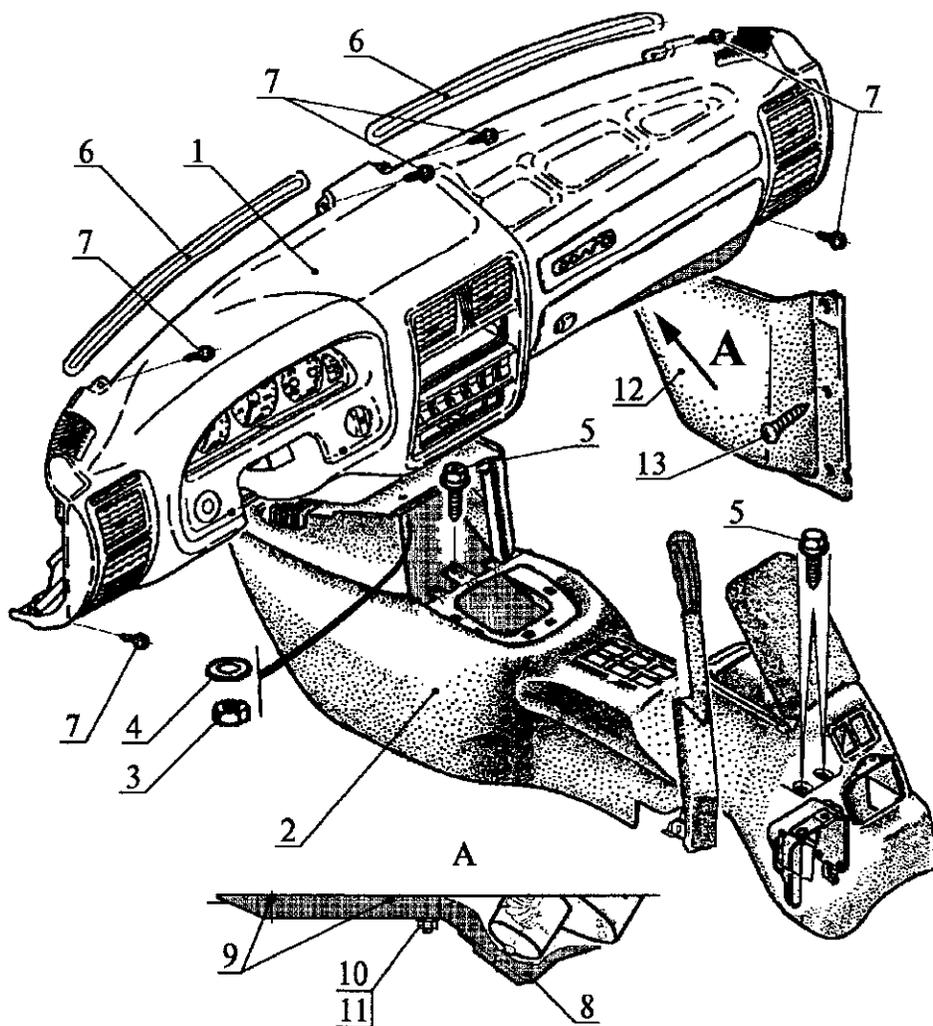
Установка панели приборов, консоли, кожуха вентилятора и панели передка боковой внутренней правой:
